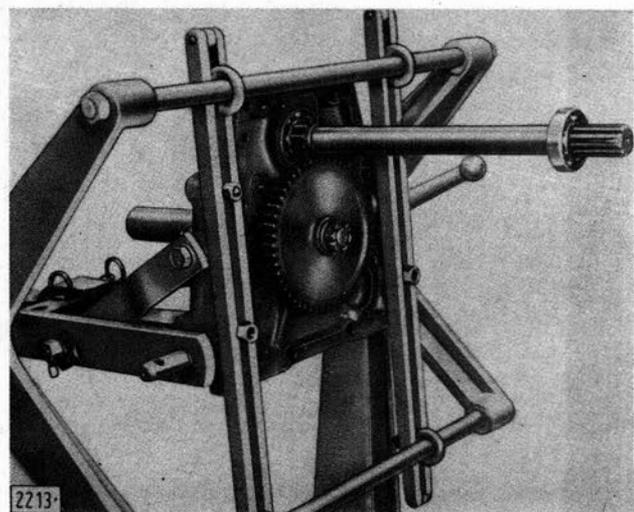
Ensemble prise de force monté sur chevalet rotatif ARR 2220. (L'ensemble est complété de la barre d'attelage).
